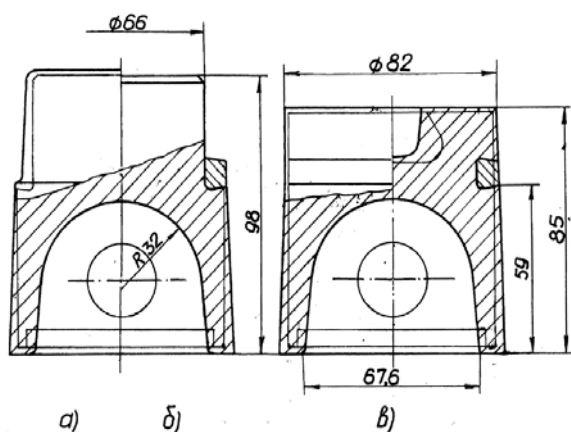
Технологические переходы штамповки биметаллической заготовки поршня.
